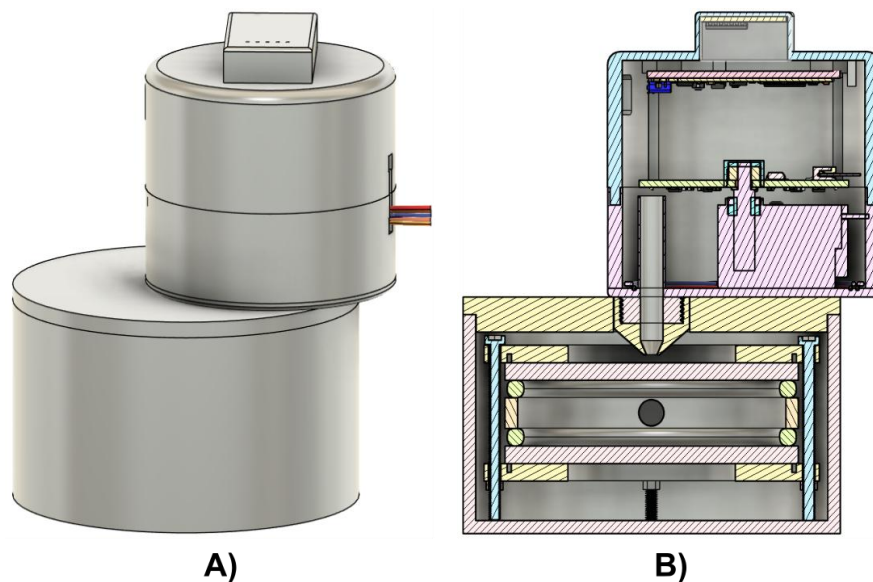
Diseño del ensamble de la fuente de luz con la celda fotoacústica. A) Vista general del diseño (en la parte superior se muestra la fuente de luz y en la parte inferior la celda fotoacústica) y B) Sección transversal del montaje de la fuente de luz led y la celda fotoacústica. Elaboración propia (2025).
